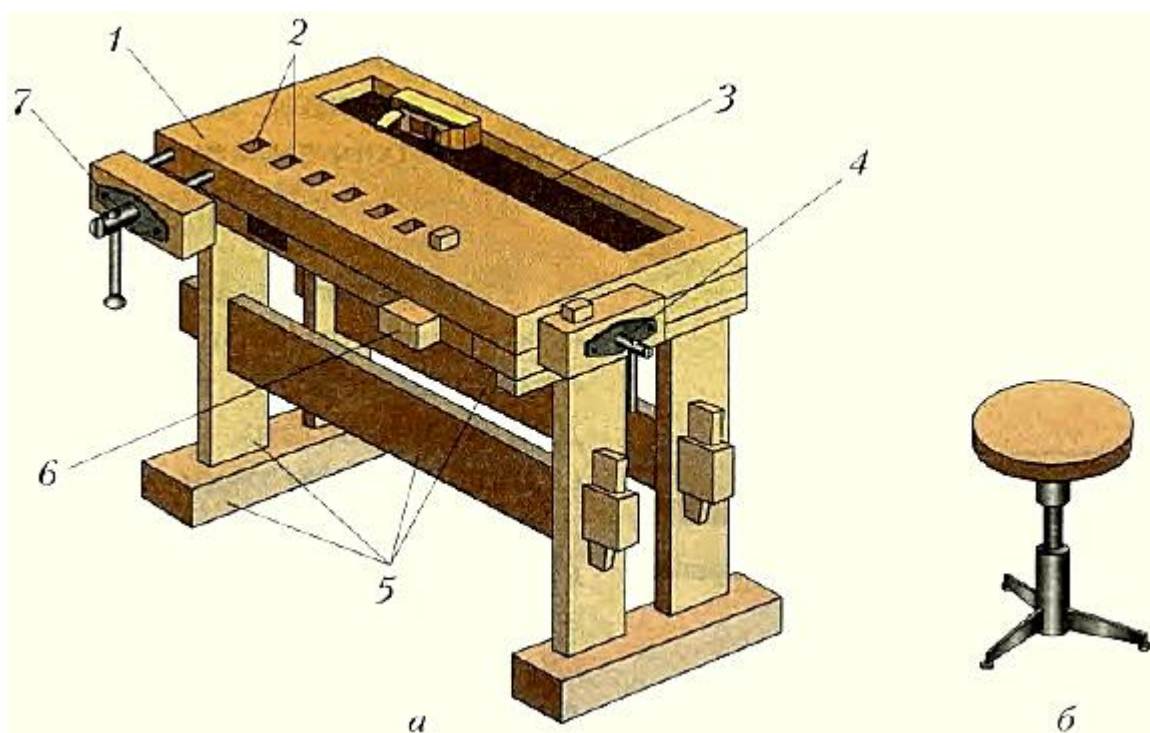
Столярный верстак (а): 1 — крышка; 2 — отверстия для клиньев; 3 — лоток; 4 — задний зажим; 5 — подверстачье; 6 — выдвигная опора; 7 — передний зажим; стул (б)
